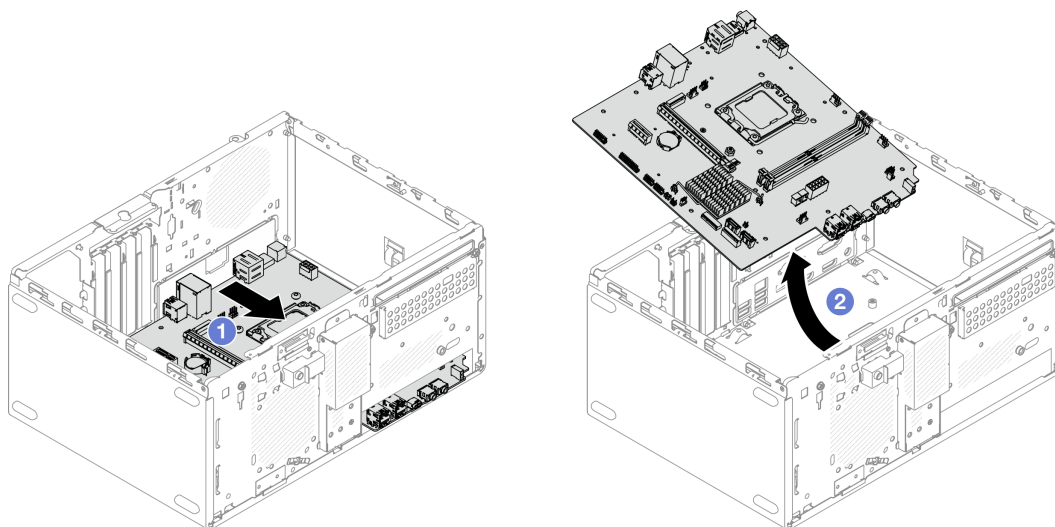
Entfernen der Systemplatine aus dem Gehäuse
